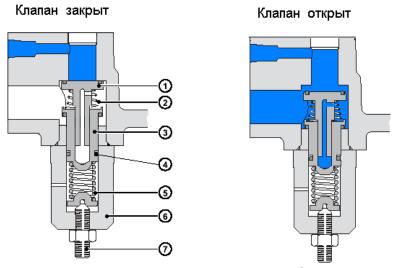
Схема клапана минимального давления: 1 — тарелка обратного клапана; 2 — пружина обратного клапана; 3 — поршень; 4 — кольцо уплотнительное; 5 — пружина клапана минимального давления; 6 - корпус; 7 — винт регулировочный.
